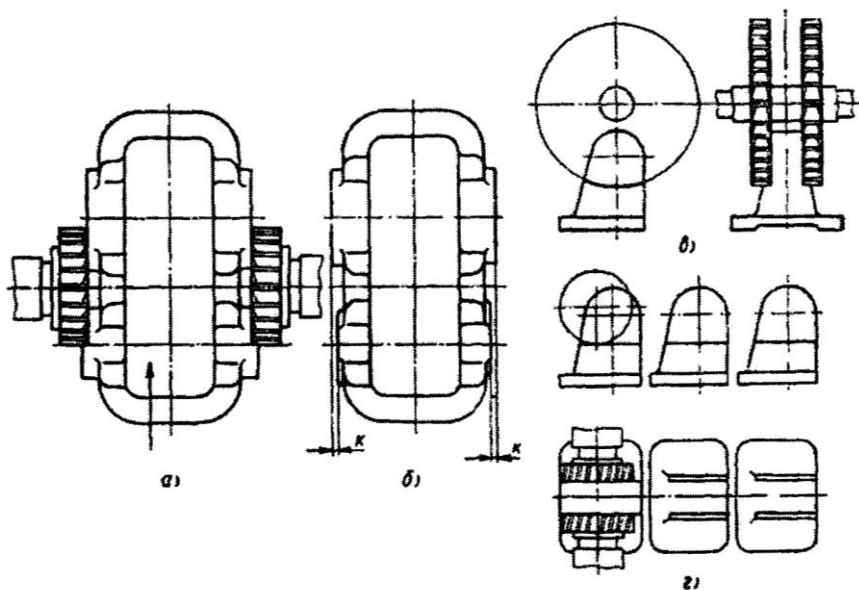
Конструктивні рішення корпуса редуктора
